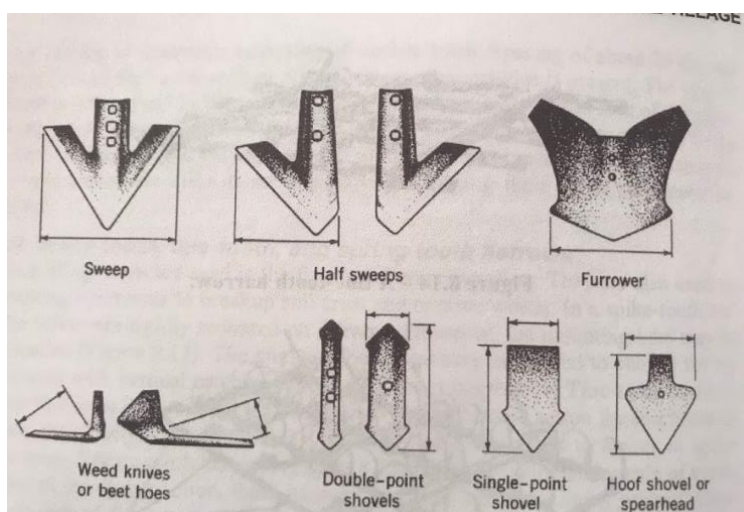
Ulike spisser for bruk ved primær jordbearbeiding. Bildet er hentet fra fra *Engineering Principles of Agricultural Machines* (2006)
